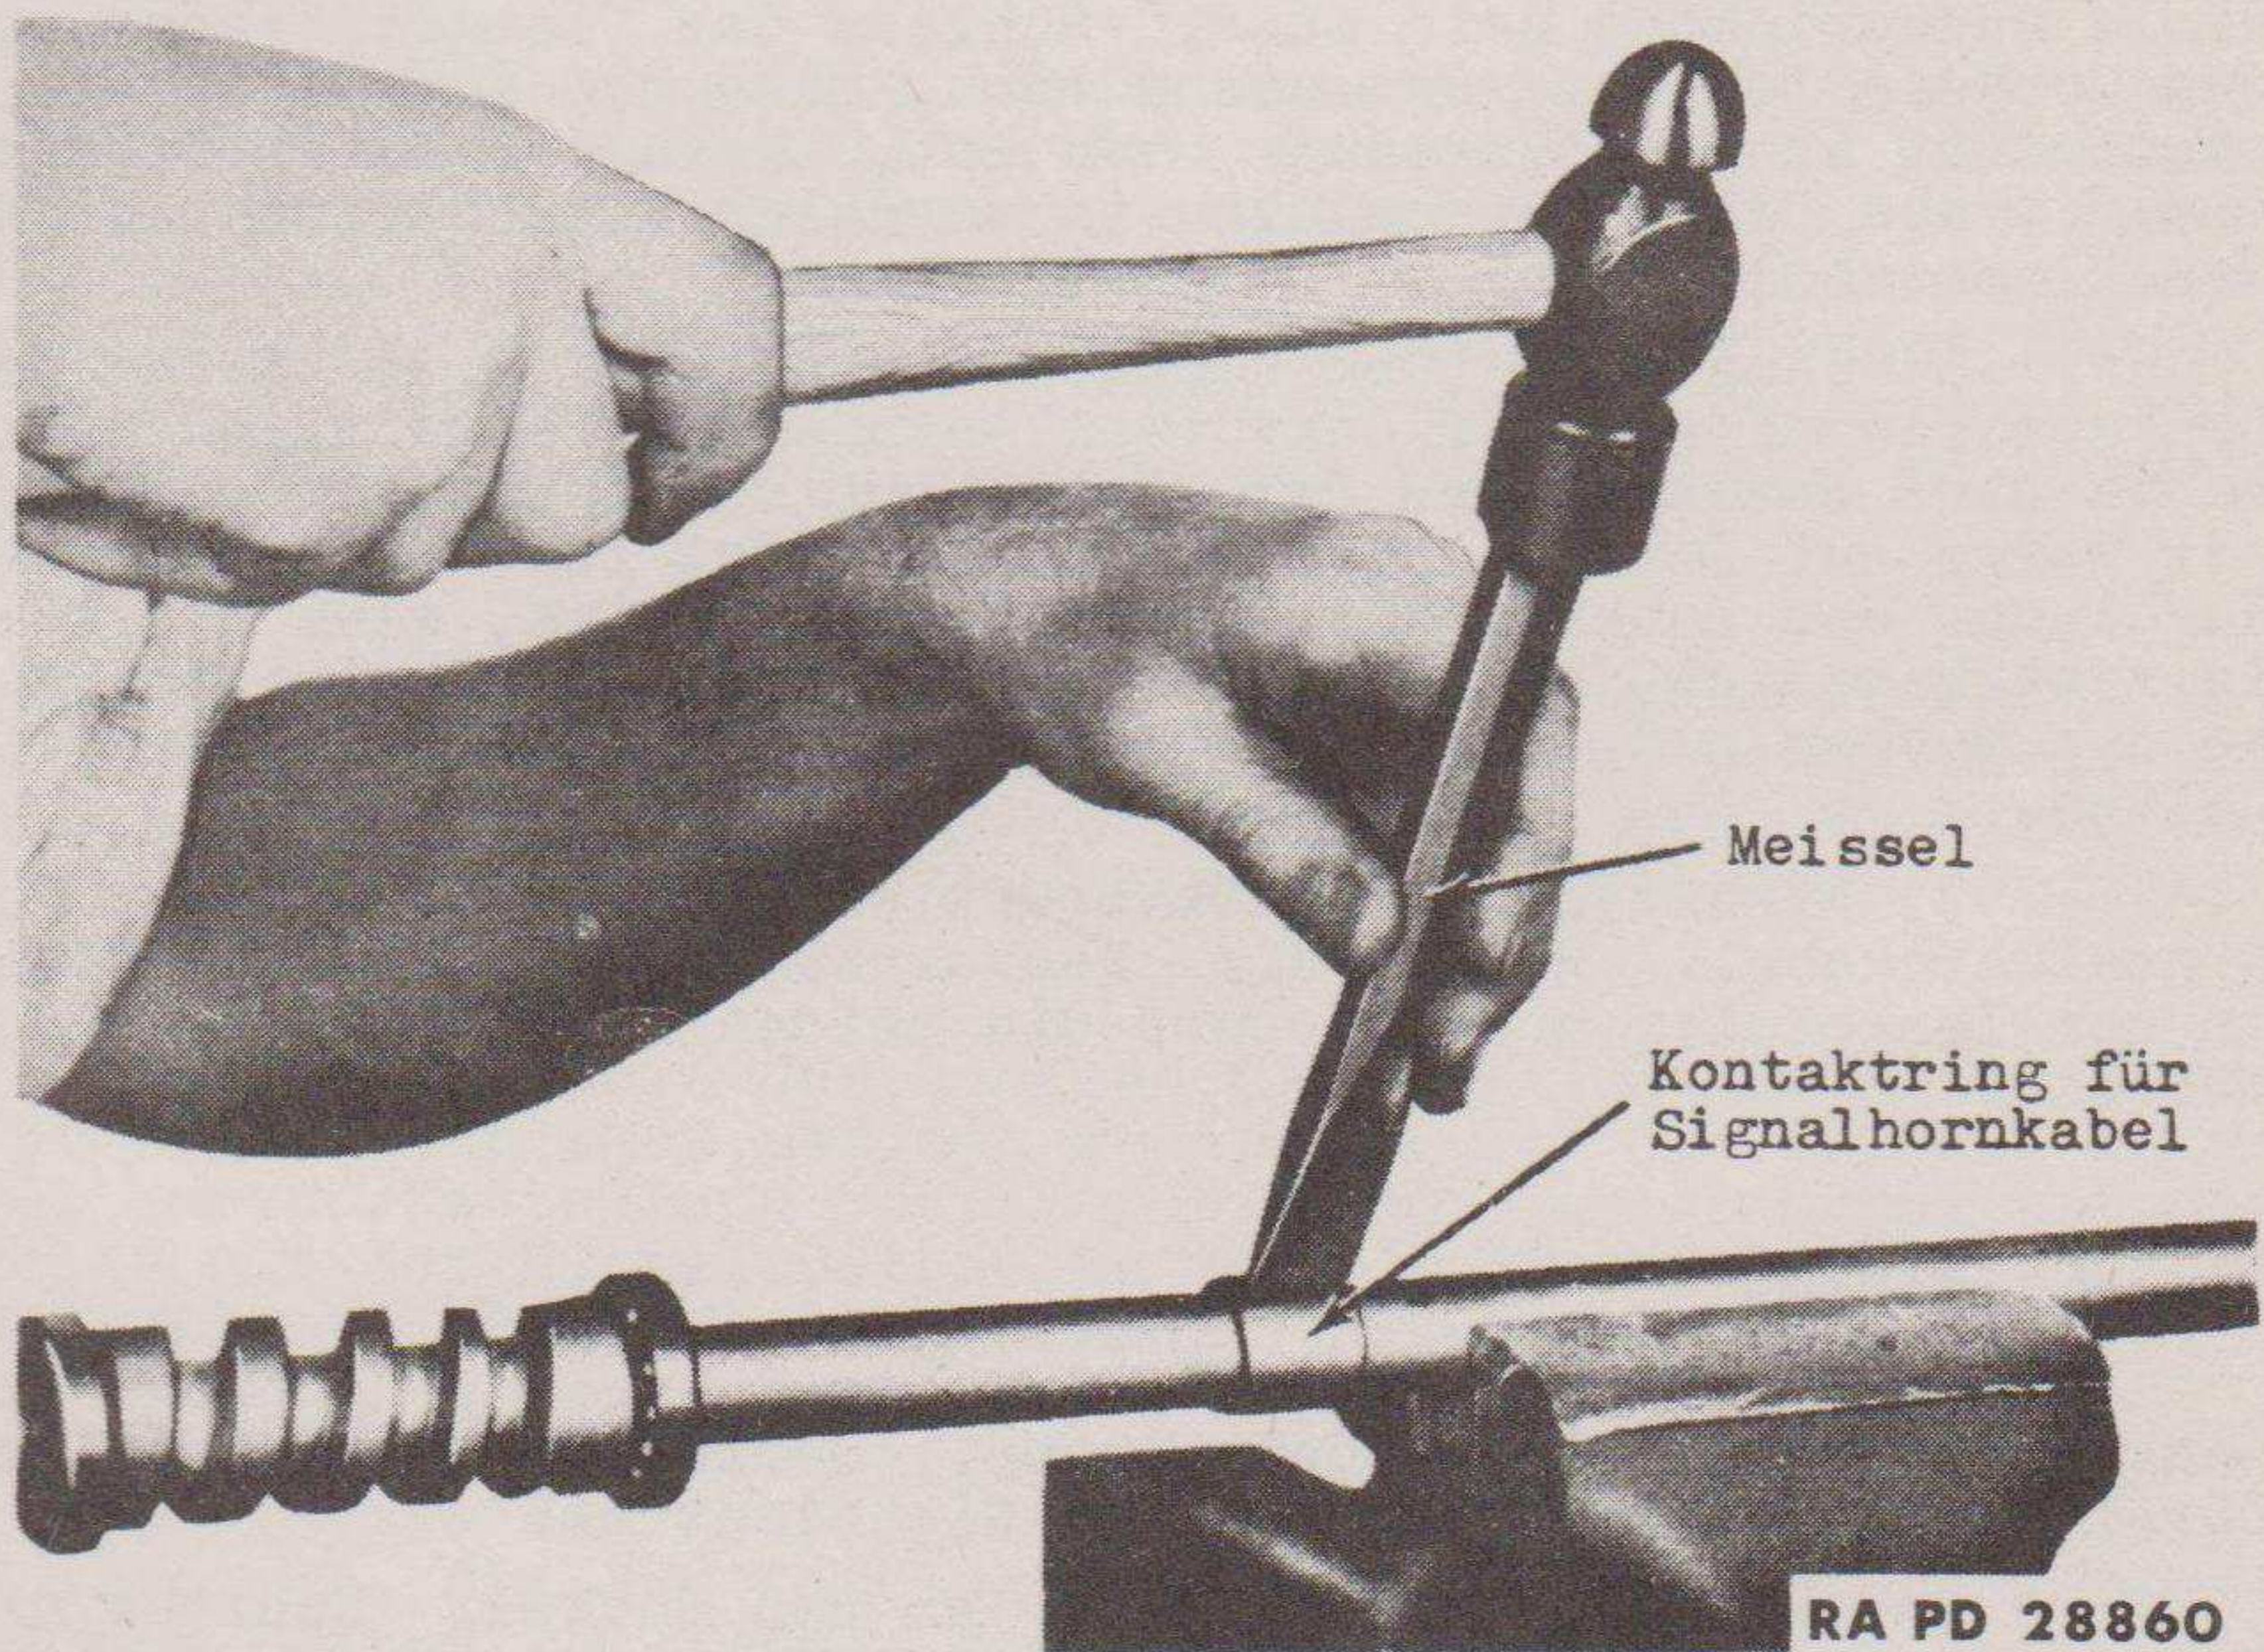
Entfernen des Kontakttringes für Signalhornkabel
